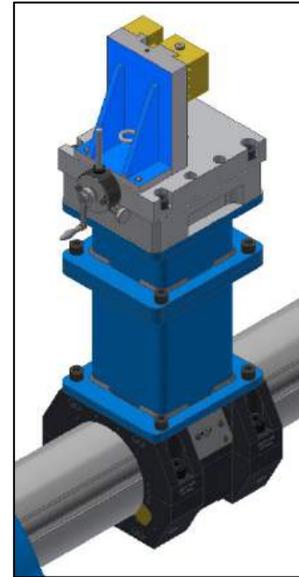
Planfräskopf mit Abstandshaltern am Werkzeugträger montiert
